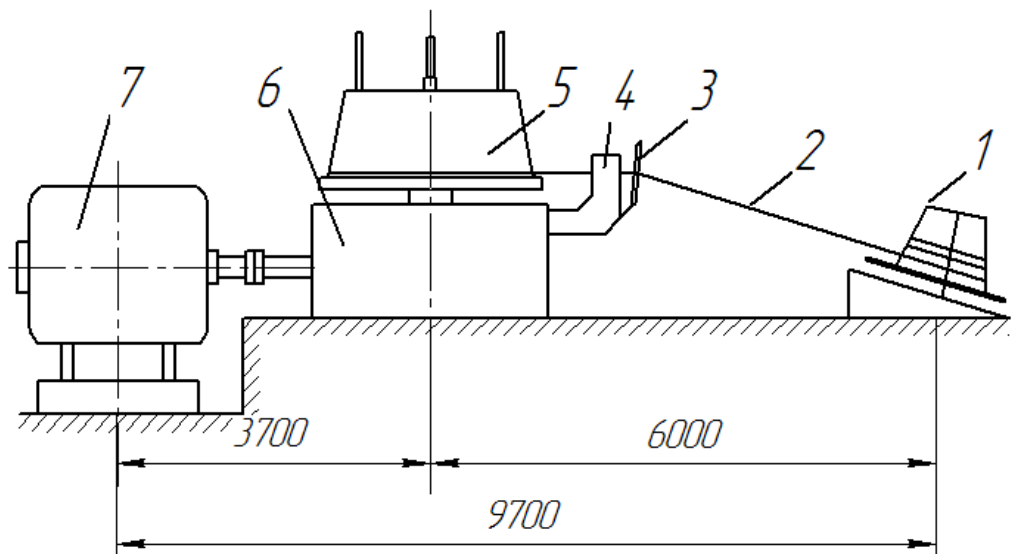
Схема стана одноразового волочіння: 1 - розмотувач; 2 - заготовка (катанка); 3 – запобіжне кільце; 4 - волокотримач із волокою; 5- тягнучий барабан; 6 – конічно-циліндричний редуктор; 7 - електродвигун постійного струму.
